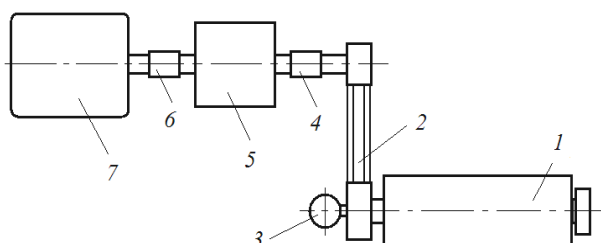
Схема агрегування приводу головного руху верстата: 1 – комплектний шпindelний вузол, 2 – передача, 3 – датчик, 4 – муфта, 5 – автоматична коробка швидкостей, 6 – муфта, 7 – двигун
